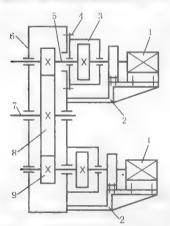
初级减速器固定式 1—电机; 2—固定支座; 3—初级减速器; 4—螺栓; 5—初级减速器输出轴; 6—悬挂整体外壳; 7—主轴; 8—末级大齿轮(从动件); 9—主动小齿轮
